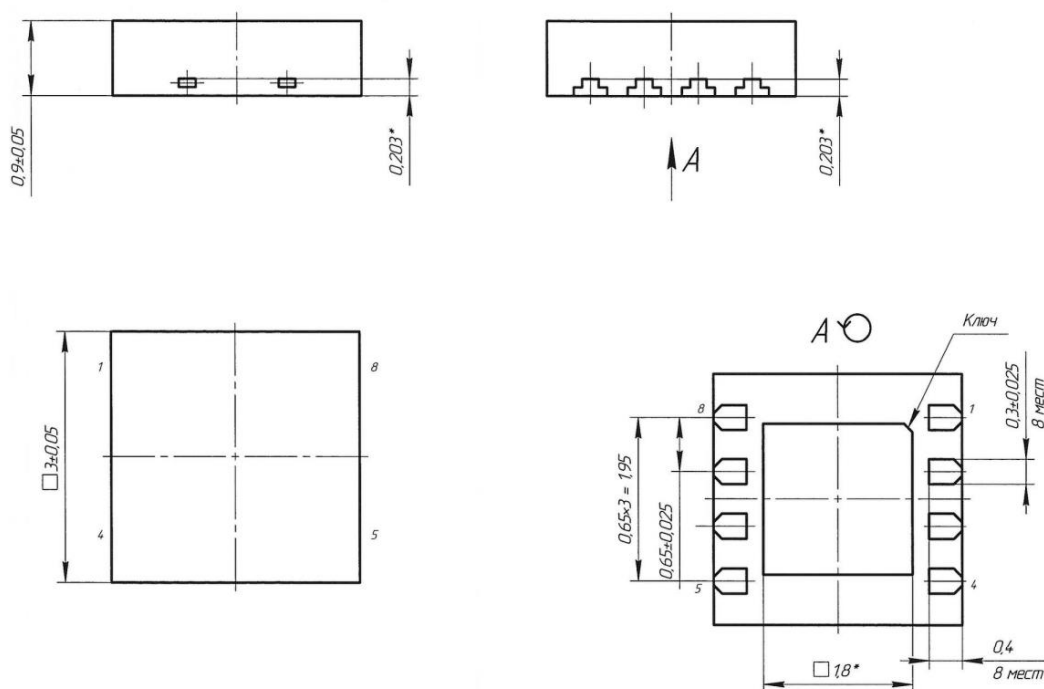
Габаритный чертеж корпуса 5241.8-1H3 К (размеры в мм)
